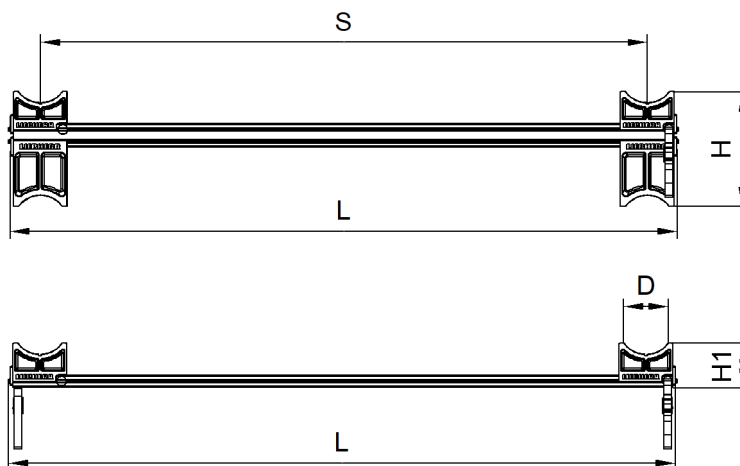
Размеры - приспособление для укладывания в штабель 2200 mm (7,22 ft)
